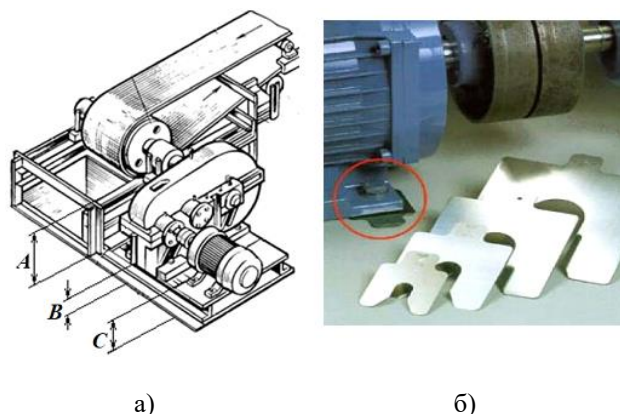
Монтаж и центровка агрегатов привода (а) с применением набора калиброванных пластин (б)
